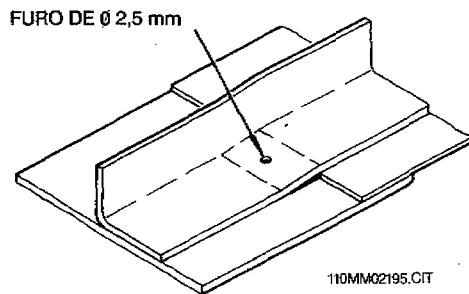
Furo para Vedação de Rebaixos muito Pequenos
